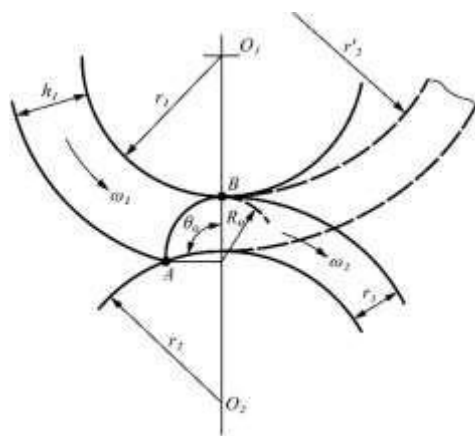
Схема деформации при прокатке с изгибом заготовки
